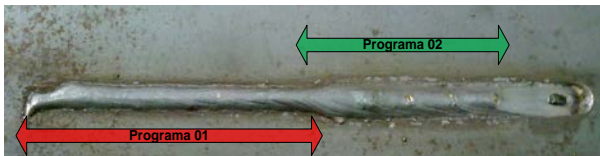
Exemplo de cordão de soldagem realizado na célula robotizada.
